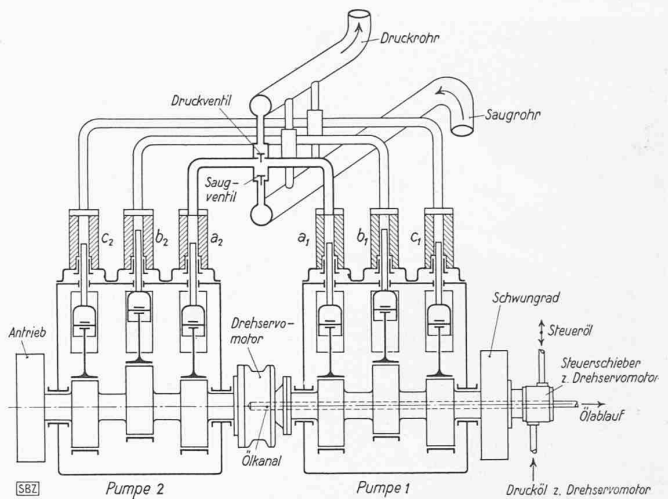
Kolbenpumpengruppe mit veränderlicher Liefermenge bei konstanter Drehzahl
